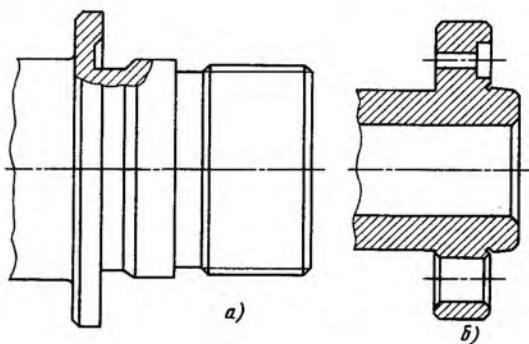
Резьбовой (а) и фланцевый (б) концы шпинделей токарных станков
